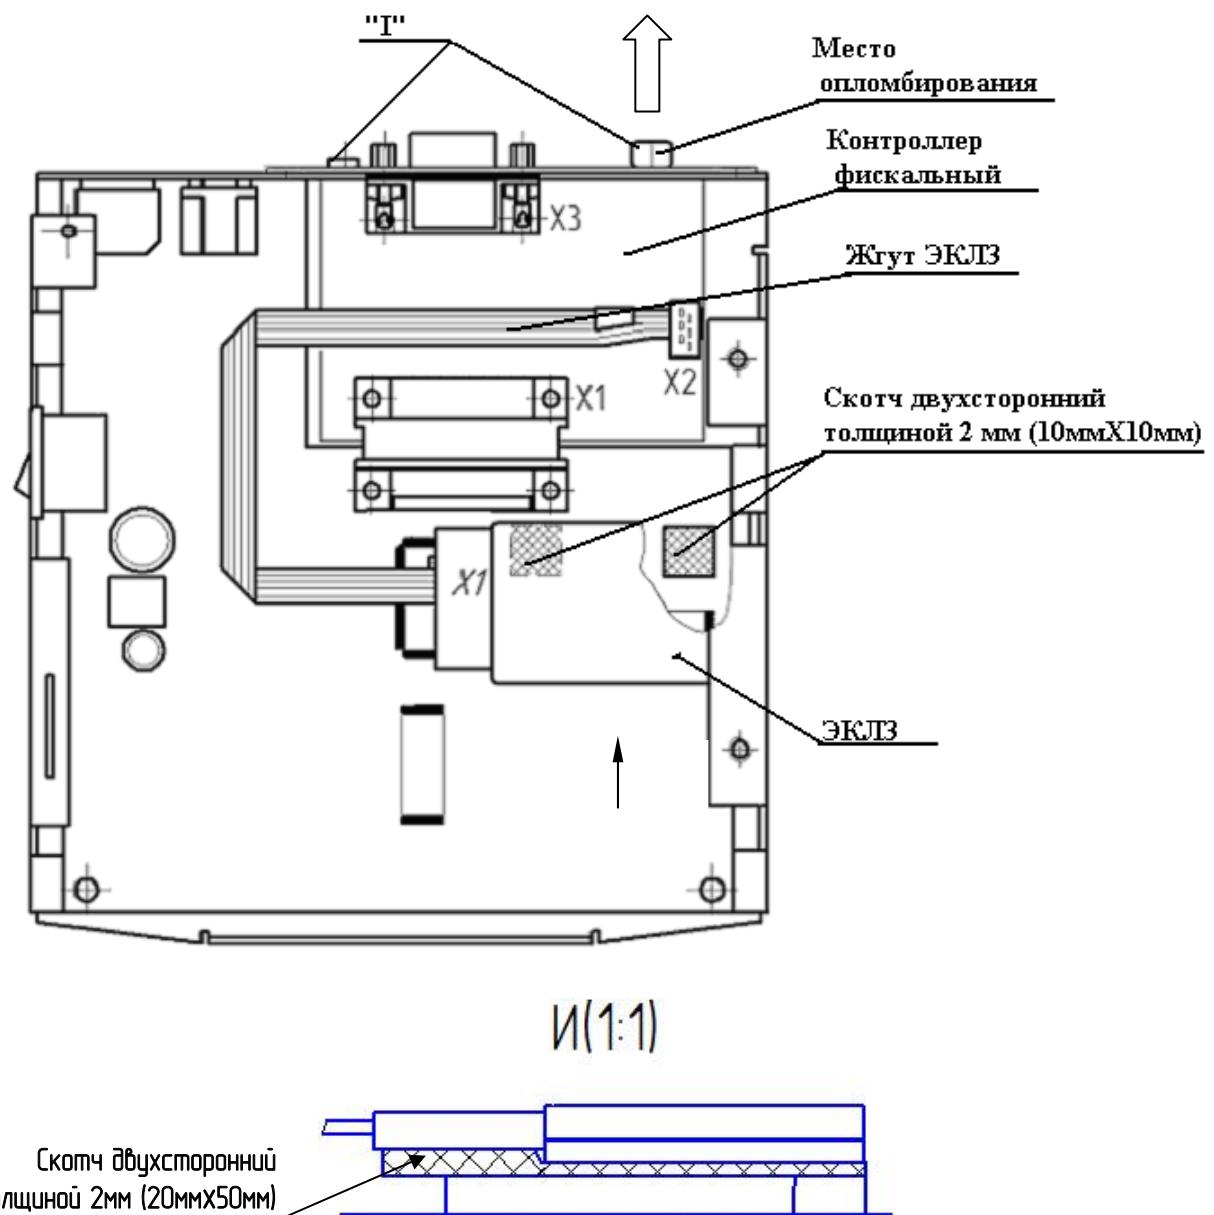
ККМ, вид сверху (без корпусной детали и чекового отсека)
